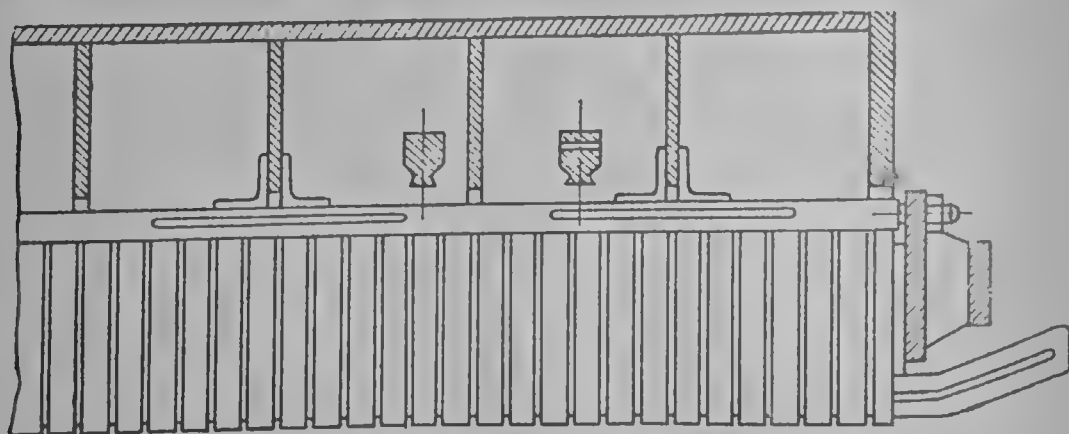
Упругая подвеска сердечника в корпусе статора при неразъемной конструкции сердечника и корпуса статора
